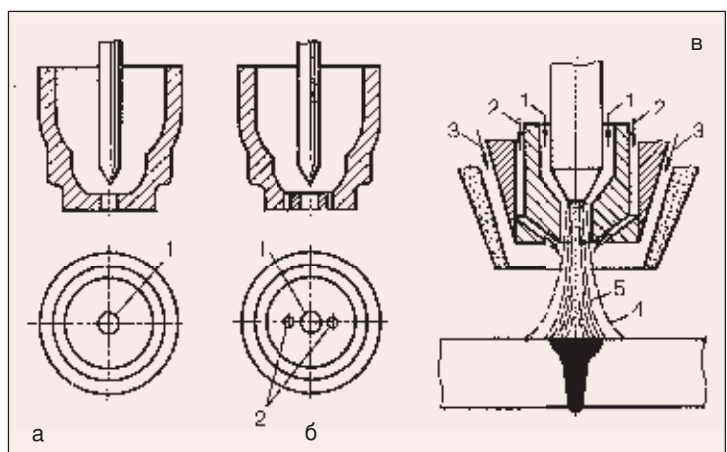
Схемы плазмообразующих сопел для сварки плазменной дугой: а — с круглым пятном нагрева; б — с вытянутым пятном нагрева (1 — центральный канал для газа, обеспечивающий образование плазменной дуги; 2 — боковые отверстия для прохода холодного фокусирующего газа); в — с дополнительным газовым потоком для фокусировки дуги (1 — плазмообразующий газ; 2 — фокусирующий газ; 3 — защитный газ; 4 — очертания дуги при отсутствии фокусирующего газа; 5 — то же с фокусирующим газом)
